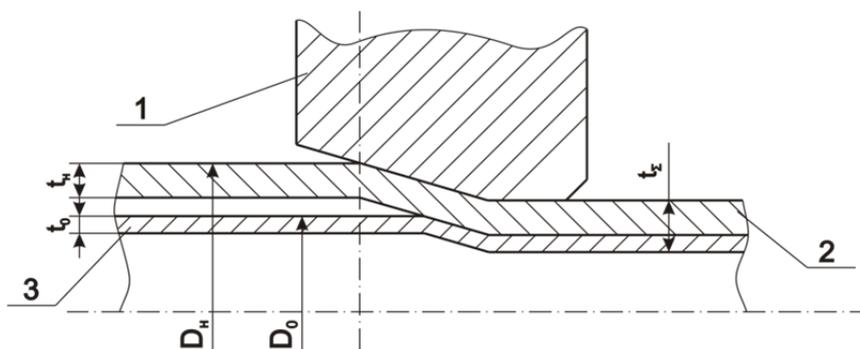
Схема сочленения двухслойной монометаллической трубы безоправочным волочением:
